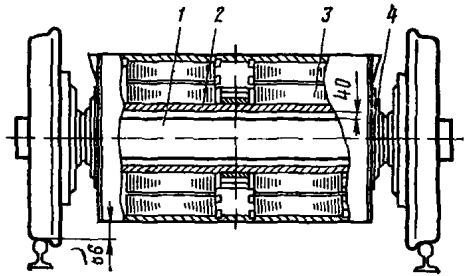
Безредукторный привод с асинхронным тяговым двигателем:
